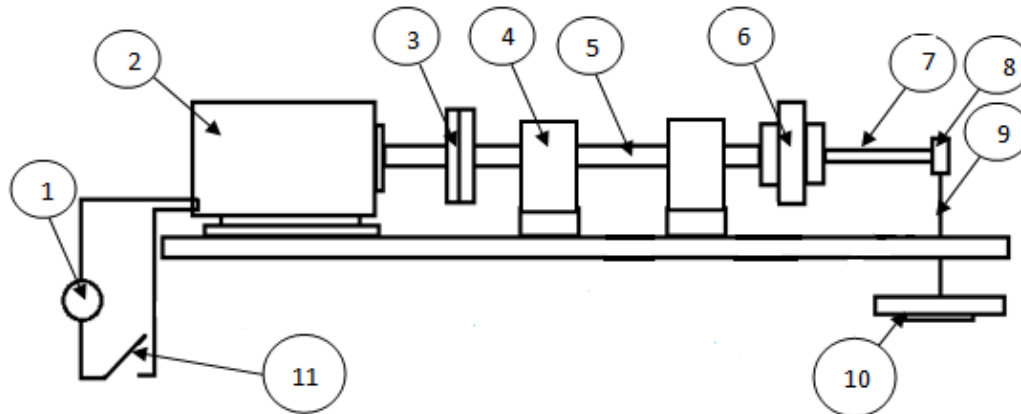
Skema Instalasi Mesin *Continuous Drive Friction Welding
